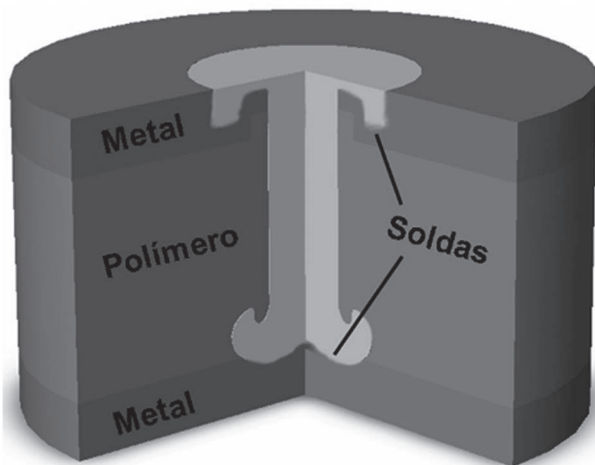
Esquema de uma possível configuração metal-polímero fabricada por FricRiveting.
